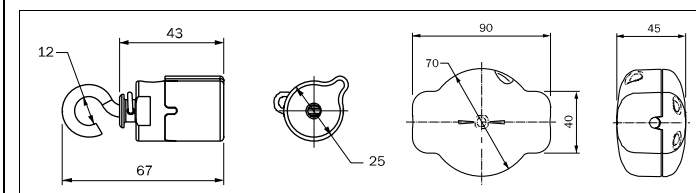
Disegno dimensionale dei morsetti per funi e della puleggia tenditrice
